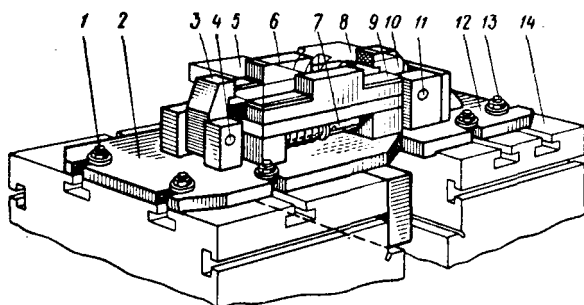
Наладка на тиски для крепления вилок при фрезеровании
